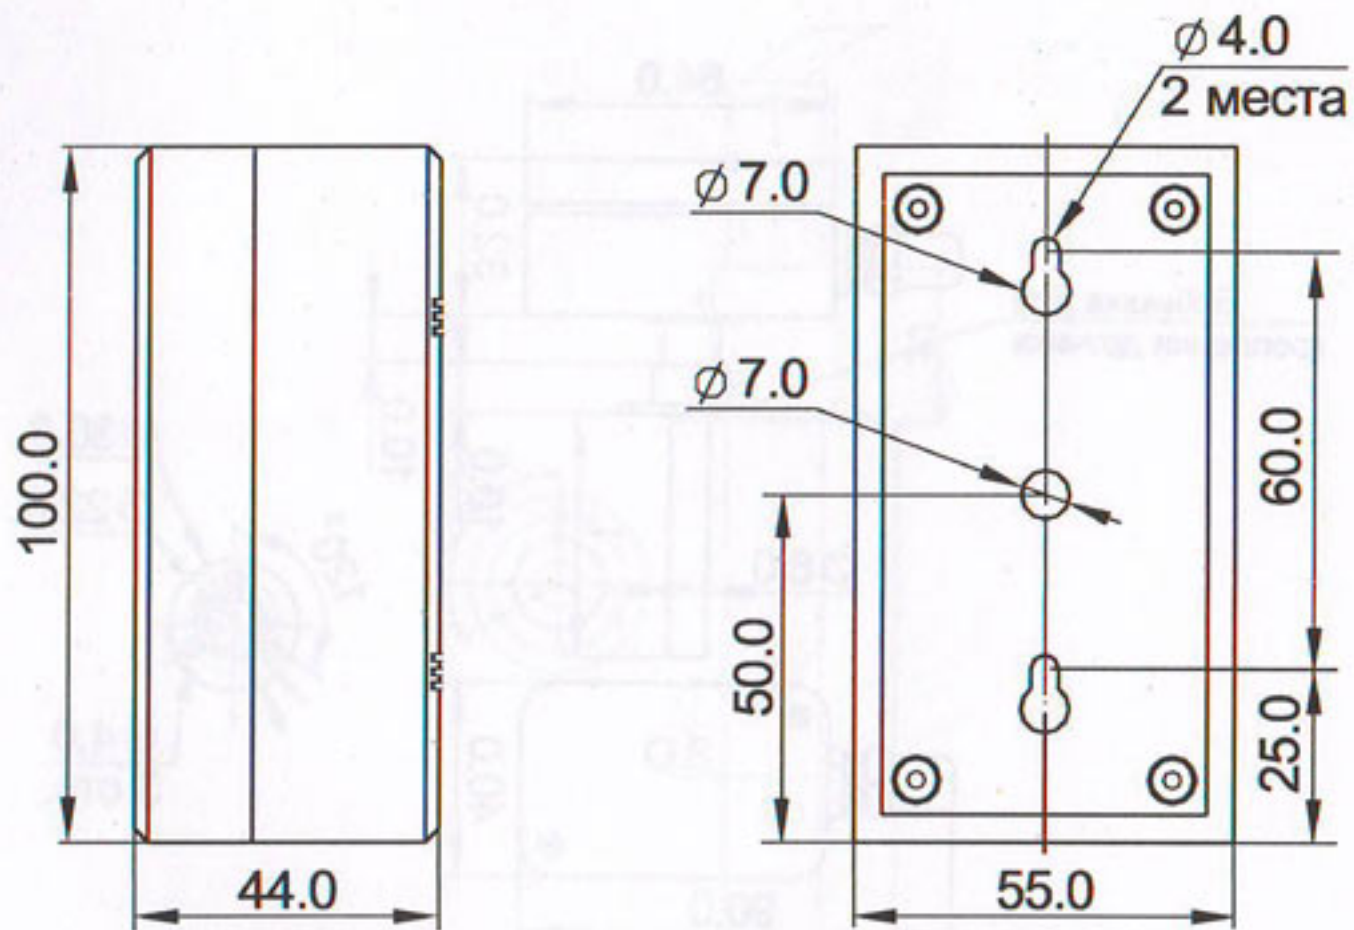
Конструктивные особенности и габаритно-присоединительные размеры датчика СТ-02
